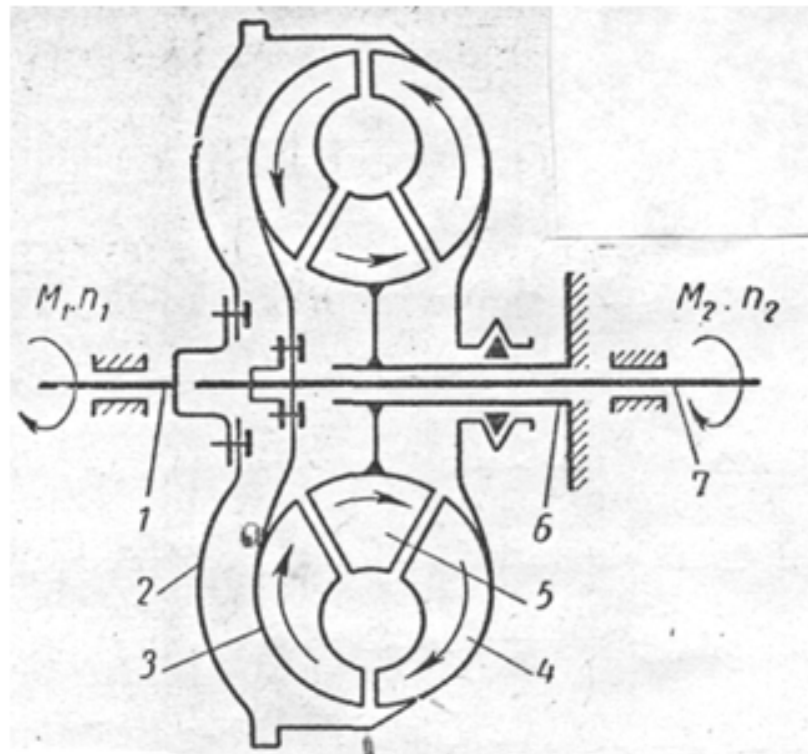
Схема одноступенчатого гидротрансформатора: 1 - коленчатый вал двигателя; 2 - корпус гидротрансформатора; 3 - турбинное колесо; 4 - насосное колесо; 5 - колесо-реактор; 6 - вал колеса-реактора; 7 - ведомый вал
